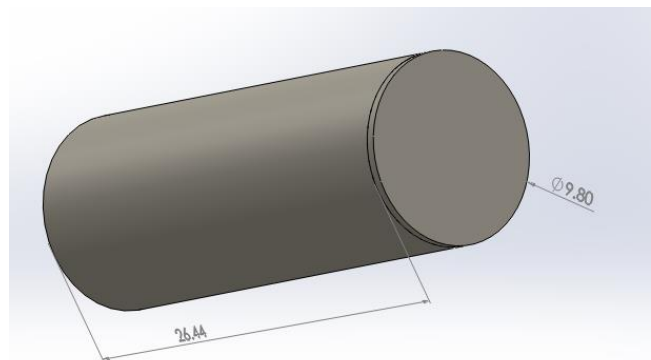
Vista frontal y lateral del tanque de almacenamiento a construir. Diseño de los autores
